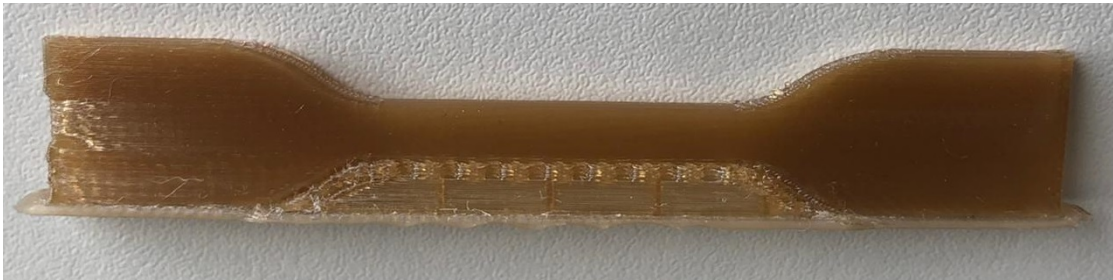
PEEK - Orientação Vertical no plano XZ
